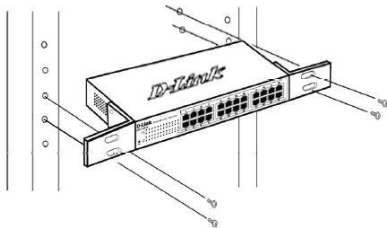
Montaggio del dispositivo DFL-260E / 860E nel rack o nel telaio
